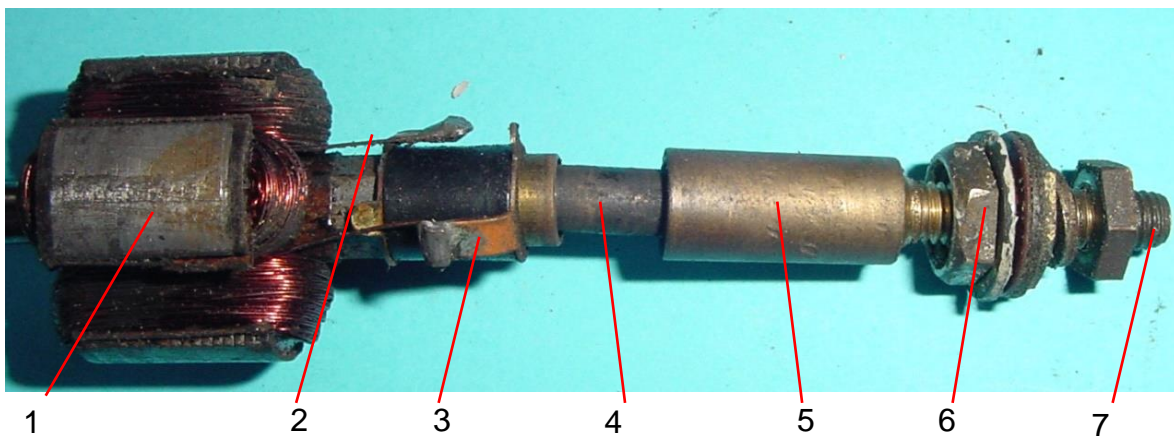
Anker und Schleifkontakt mit Kabelanschlussbolzen: 1- Ankerblechpaket (Durchmesser 24 mm, Länge 14 mm), 2- Masseanschluss, 3- Spannung führender Anschluss, 4- Kohlebürste, 5- Bürstenhalter, 6- Gewindeeinsatz, 7- Kabelanschlussbolzen
